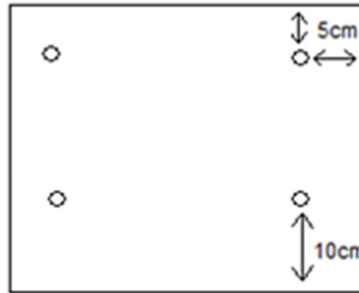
Emplacement des trous sur la plaque de plexiglass du piège fenêtre bidirectionnel
